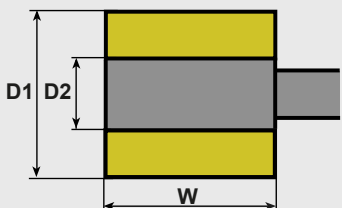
Werkzeugbeschreibung TOOL/GRIND Schleifscheibe
